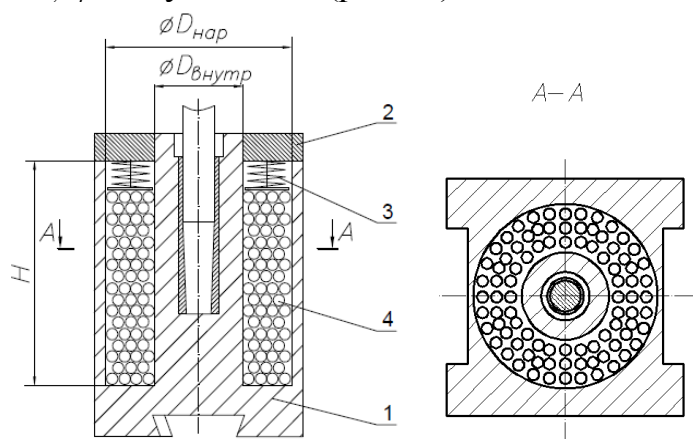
Схема бабы ковочного молота с наполнителем с внутренней кольцевой полостью: 1 – корпус бабы; 2 – крышка бабы; 3 – пружины; 4 – наполнитель (шарики)
